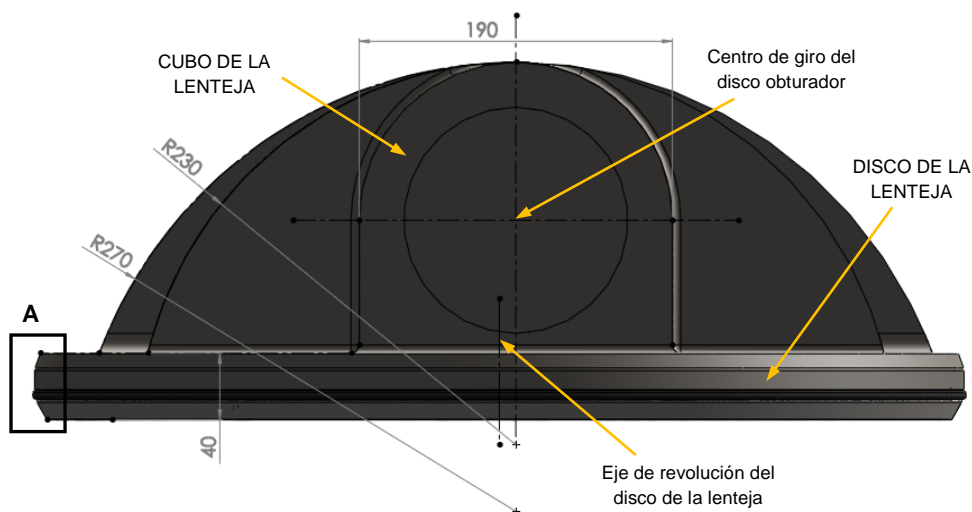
Detalles de la lenteja con dimensiones principales (en mm)
